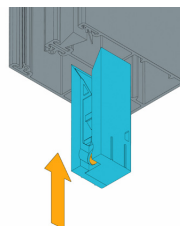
Установка стопора в шину направляющую M-GR53x39IE
